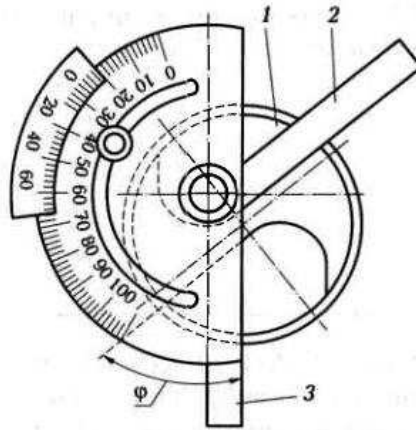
Схема измерения угла наклона поперечной кромки сверла универсальным угломером:
